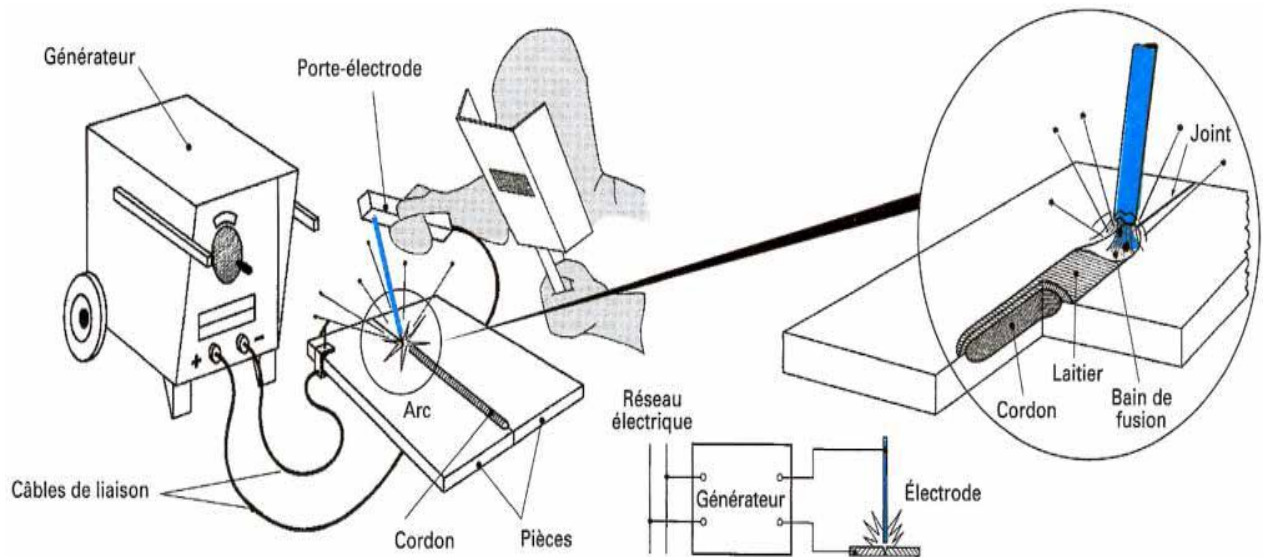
Soudage à l'électrode enrobée [8].
